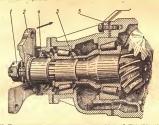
Проверка затяжки подшининков вала ведущей шестерян автомобиля ЗИЛ: 1— гайка ведущей шестерни; 2— фланец; 3— регулировочные плайы; 4— сальник; 5— регулировочные прокладки зацепления конических шестерем.
